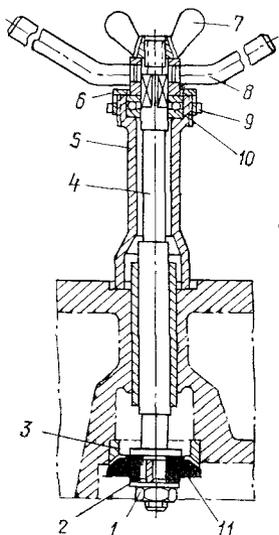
Приспособление для обработки рабочей фаски седла клапана:
